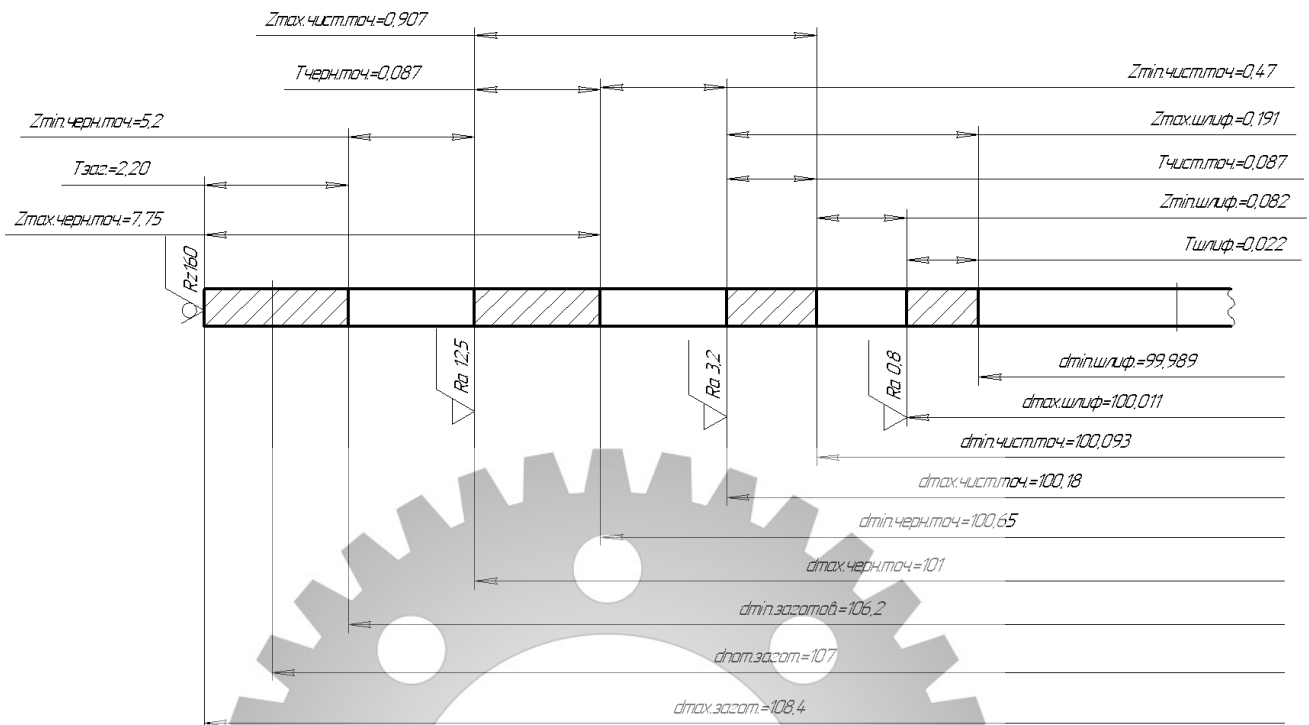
Схема розташування припусків і допусків на розмір 100js6(±0,011)
